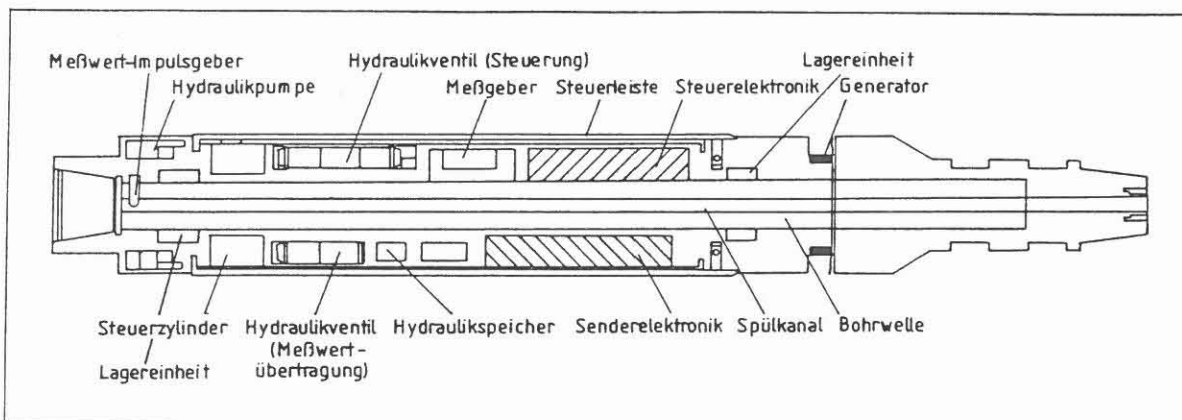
Zielbohrstange der Fa. Schwing Hydraulik
